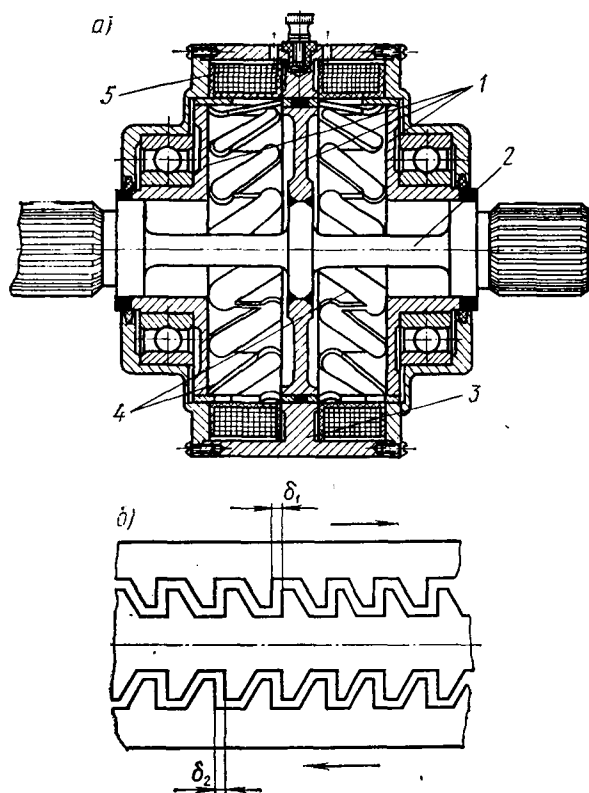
Индуктивный датчик (а) для измерения крутящего момента и его ротор (б) после фрезеровки в нем зубцов
